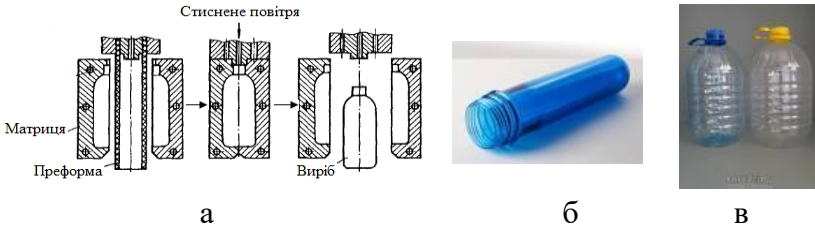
Схема пневматичного формування: а – послідовність операцій; б – пресформа; в – виріб
